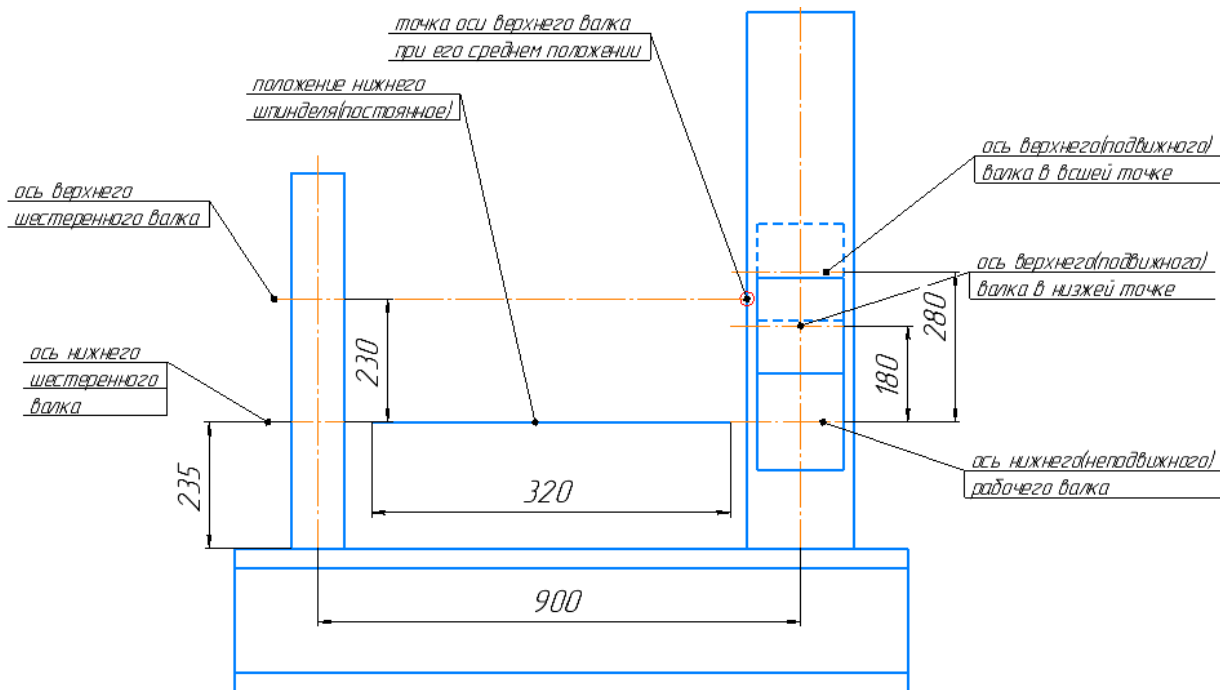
Положение оси верхнего шестеренного вала шестеренной клетки
